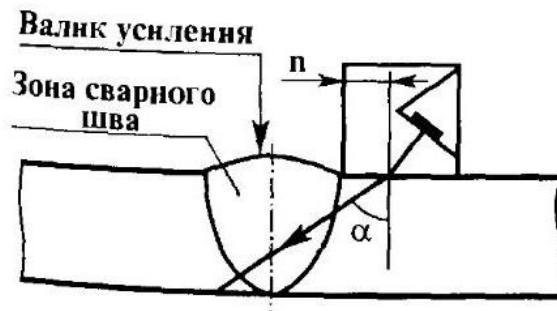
Расположение ПЭП при контроле сварного шва.
